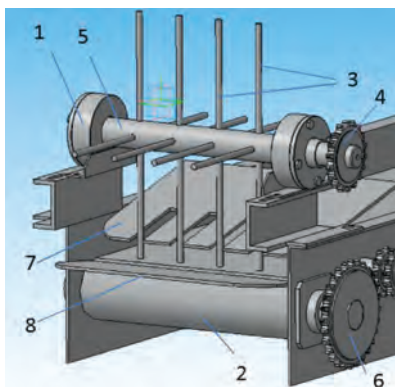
Конструкційно-технологічна схема робочих органів роторного розкидача із ущільнювальною і напрямляльною пластинами (щитками): 1 – ротор; 2 – поперечний стрічковий транспортер кормороздавача; 3 – пальці пруткові; 4 – зірочка ведена; 5 – вал ротора; 6 – зірочка тягова; 7 – регульований похилий щиток; 8 – напрямний щиток
